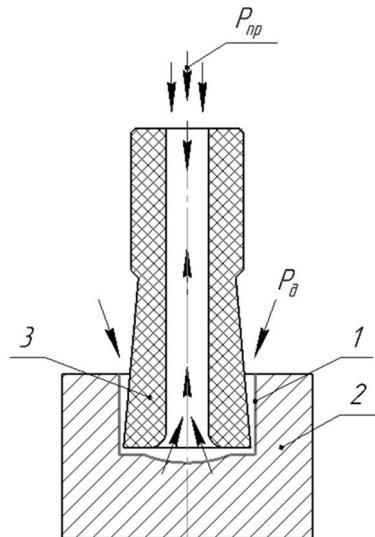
Схема формоутворення чистової обробки по внутрішньому контуру
